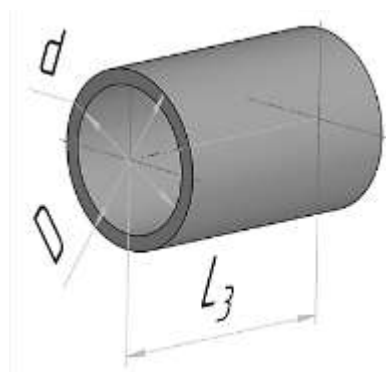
Схема рабочего зазора подшипника скольжения
